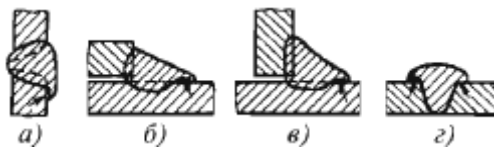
Наплывы в швах: а - горизонтальном; б - нахлесточного соединения; в - таврового соединения; г - стыкового соединения или при наплавке валиков.
